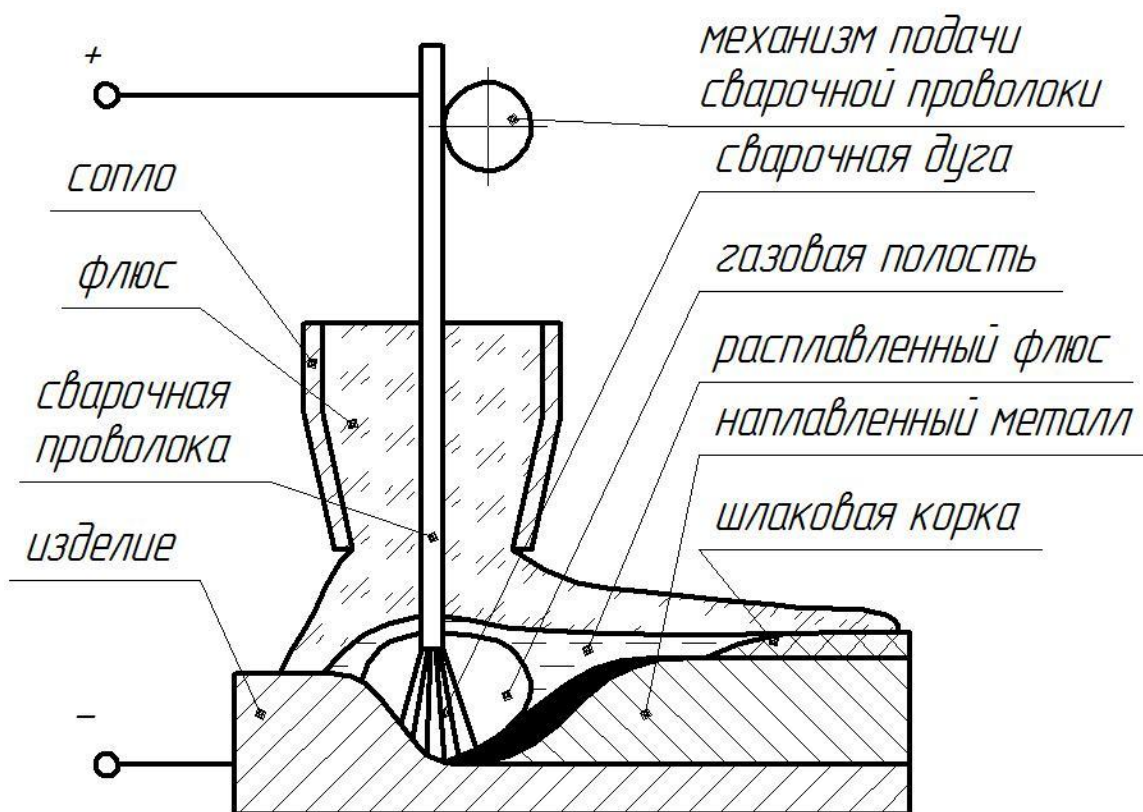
Схема процесса наплавки под слоем флюса
